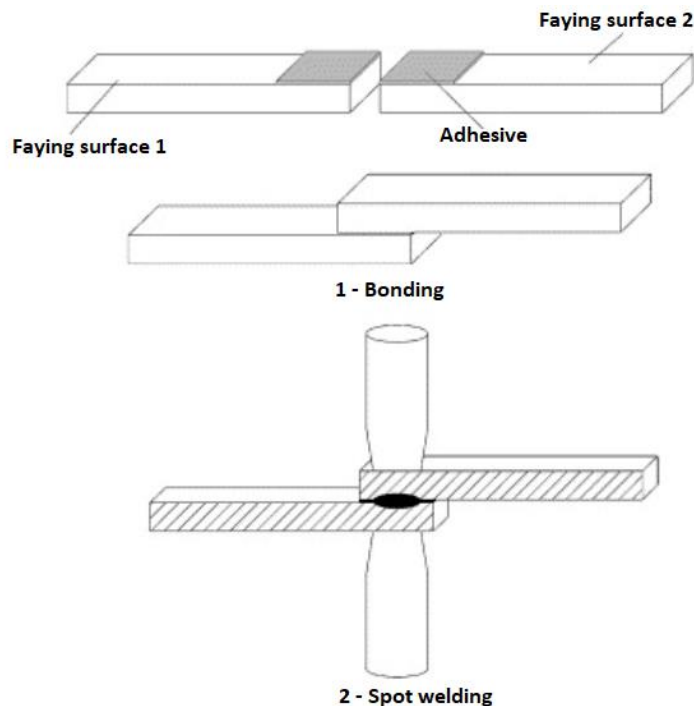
Processo ligação de juntas adesivas-soldadas através da técnica “weld-through” [69]
